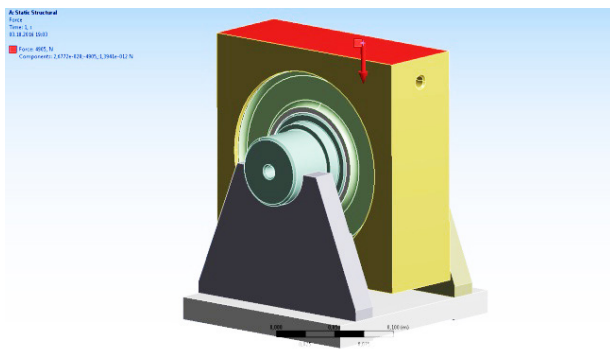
Нагружение кольца резинометаллического нагрузкой Q_1 (4905 Н)
